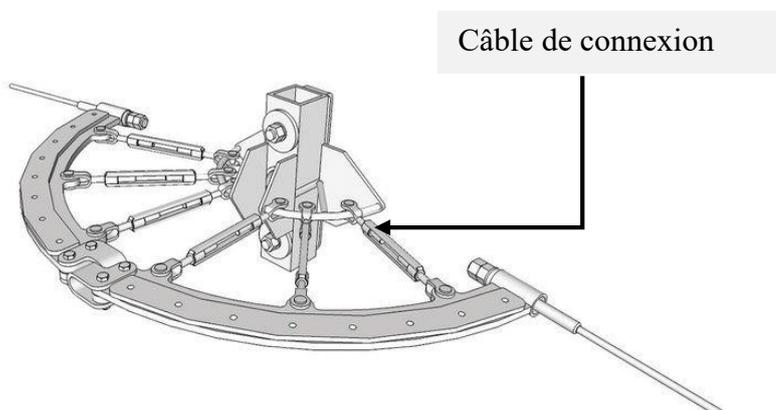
Fixation des câbles de connexions sur le poteau métallique au centre
